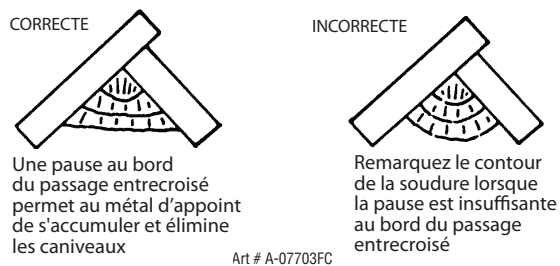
Exemples de soudure d'angle verticale
